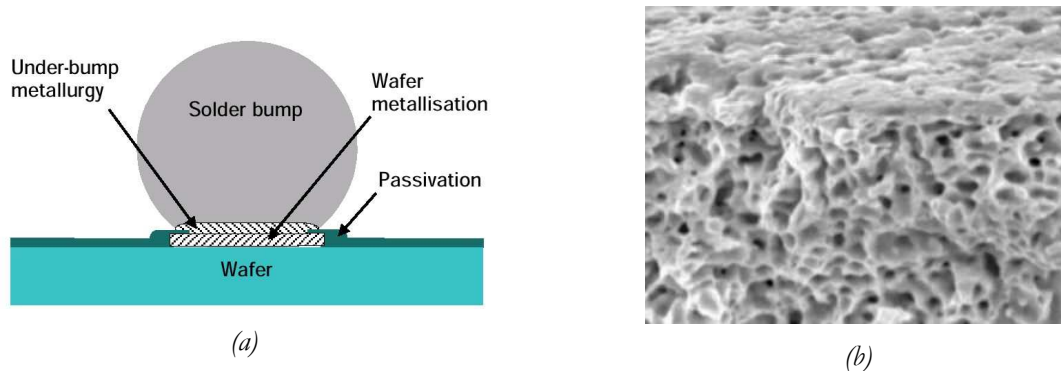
Bille de soudure, connexions et UBM (Under Bump Metal) [Wen01]
